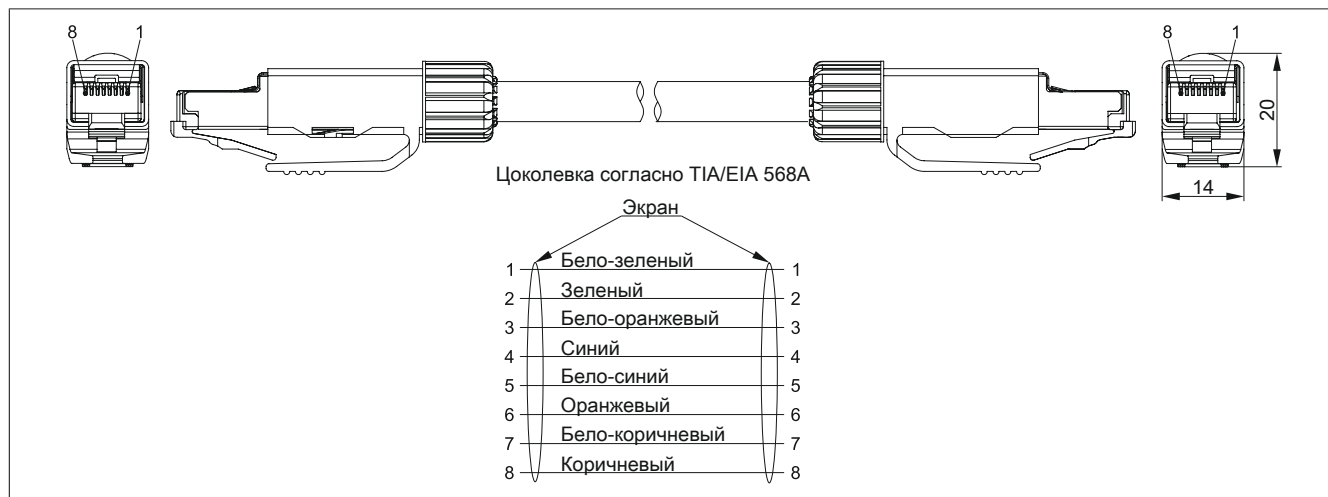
5CASD3.xxxx-00 — цоколевка
